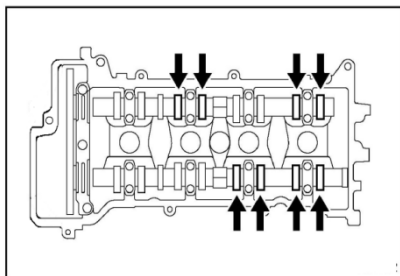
Измерение клапанного зазора для цилиндра 4 в ВМТ
